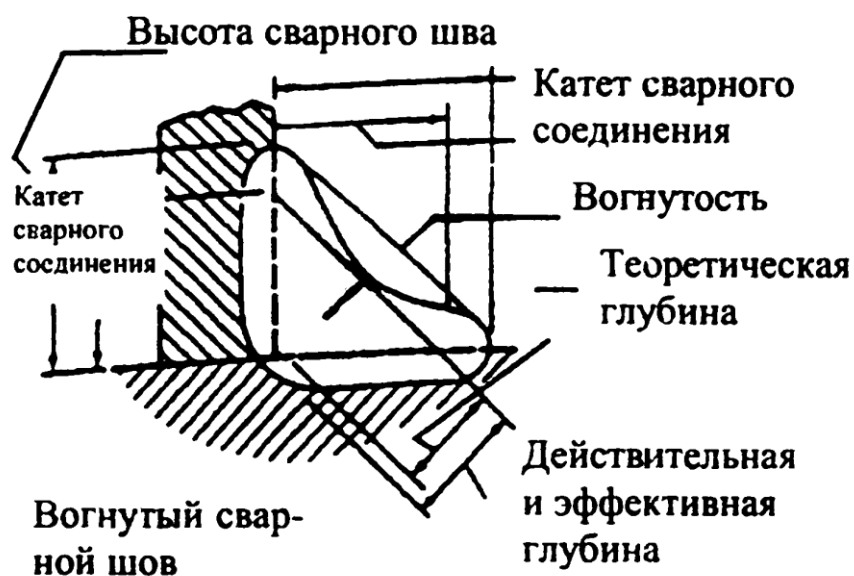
Поперечное сечение валика углового сварного шва
